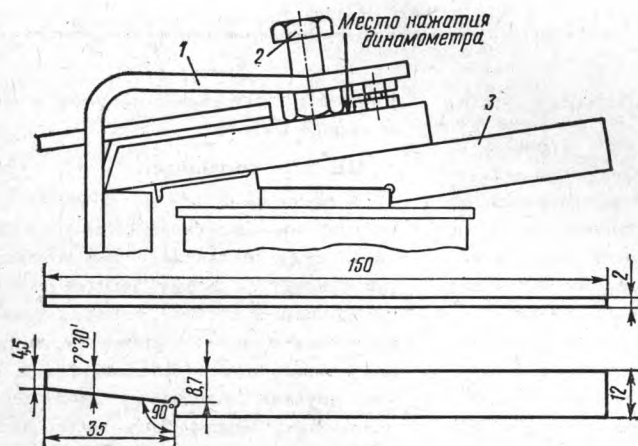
Схема регулировки зазора между якорем и ярмом реле переходов на тепловозе ЧМЭЗ контрольным калибром: 1 — ограничительный лист; 2 — регулировочный болт; 3 — контрольный калибр
